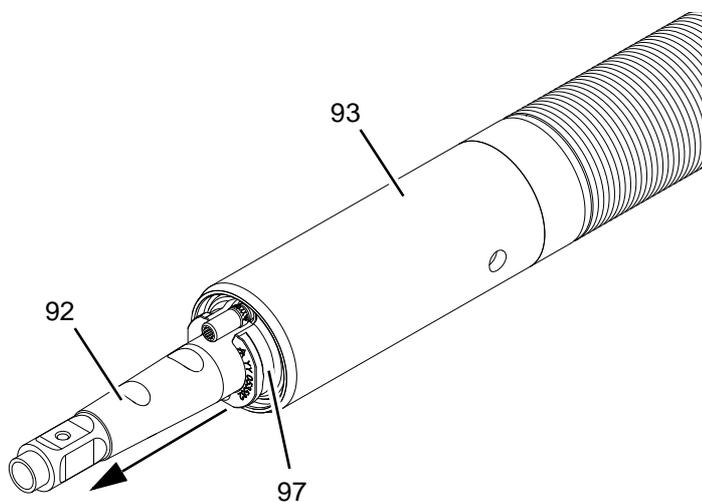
Dévisser et ôter manuellement le carter de serrage
